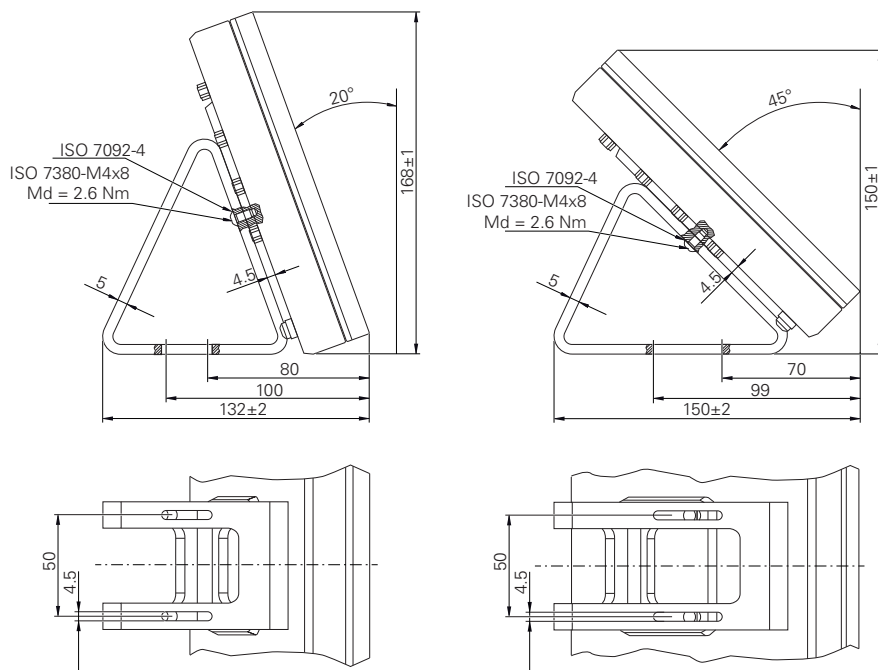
Dimensiones del aparato con pie de soporte Duo-Pos
